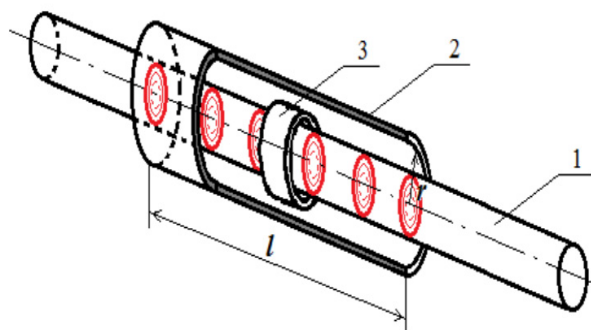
Контроль цилиндрического стержня наружным проходным вихревым преобразователем:
